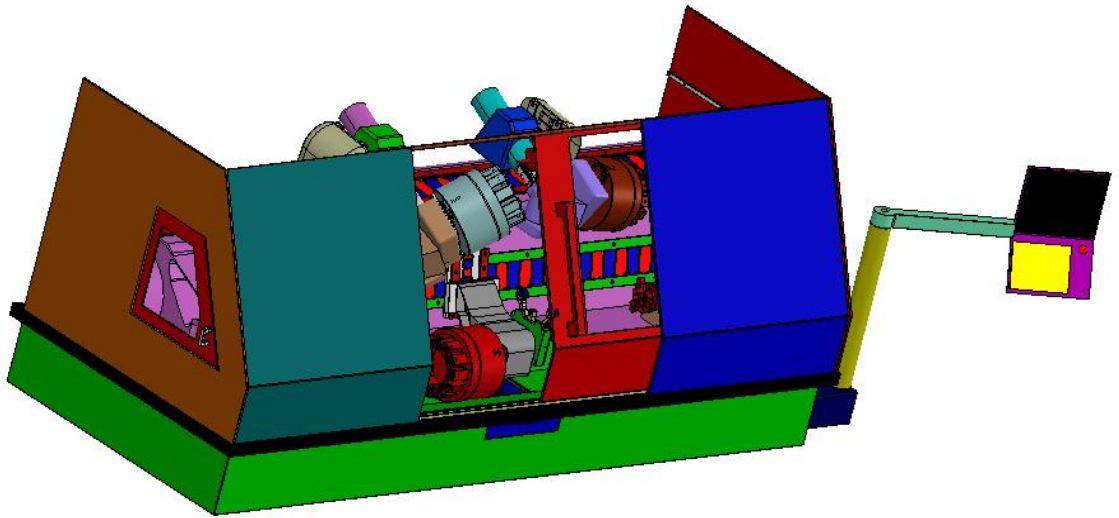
3D модель сборки токарно-фрезерного станка с кабинетной защитой
